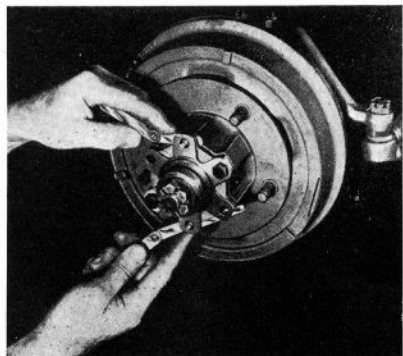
Vérification du jeu axial de l'arbre des roues—arrière.
